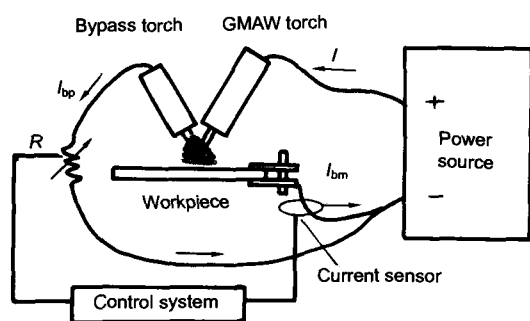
DE-GMAW 高速焊接工艺原理示意图
